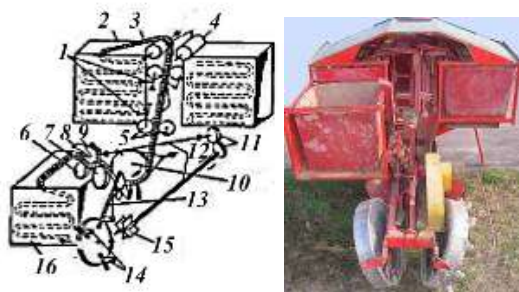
Схема лесопосадочного автомата: 1 – пружины; 2 – контейнер; 3 – кассетный сеянцедержатель; 4 – направляющий валик; 5 – ролик; 6, 7 – прижимные ролики; 8 – отсекабель; 9 – ведущая звездочка; 10 – ролик профильный; 11 – зубчатые колеса; 12 – вал привода; 13 – посадочный аппарат; 14 – упор; 15 – привод протяжки; 16 – контейнер с обработанной кассетой
